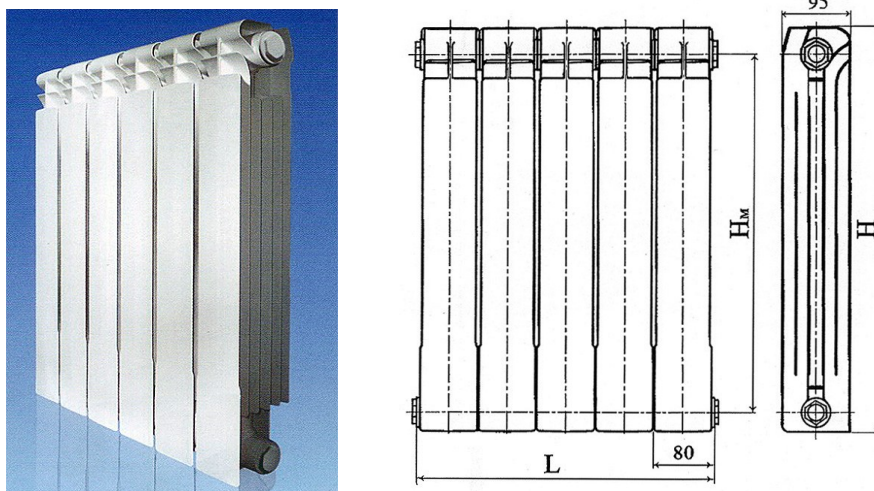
Общий вид биметаллического радиатора РБС-500/95 с боковым расположением присоединительных патрубков. Базовая модель.
